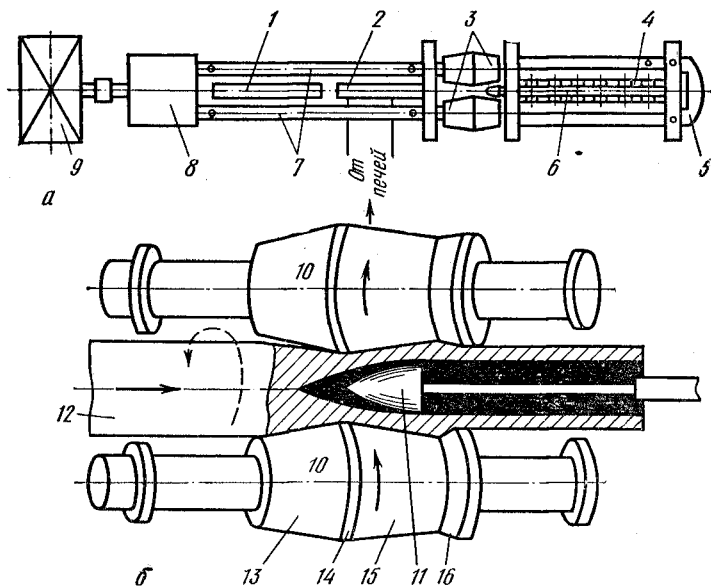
Схема прошивки трубной заготовки на прошивном стане с бочкообразными валками.
